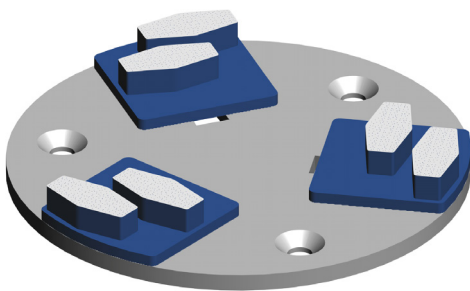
Scan-On-Befestigungsscheibe mit Werkzeugen.
